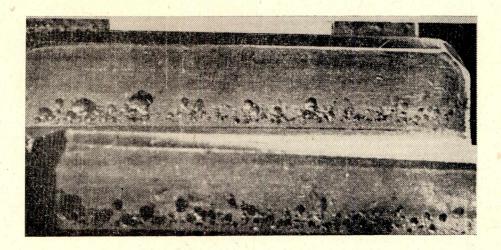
Состояние рабочей поверхности зубчатого колеса
